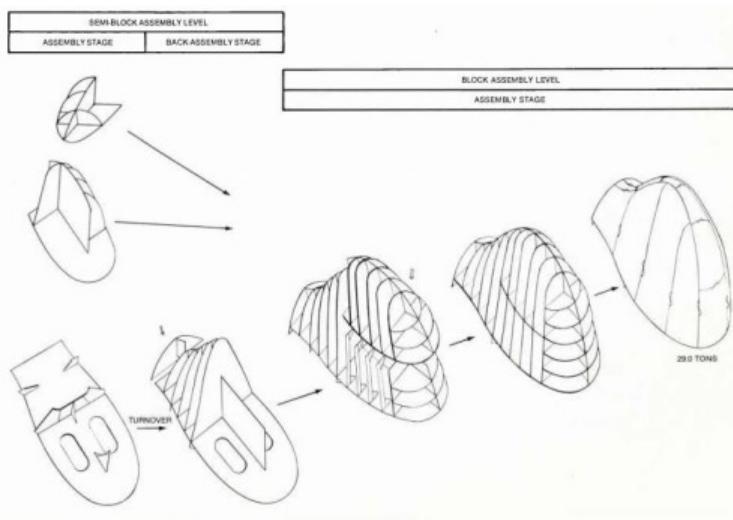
Block Assembly and Grand-block Joining pada Cant Block
